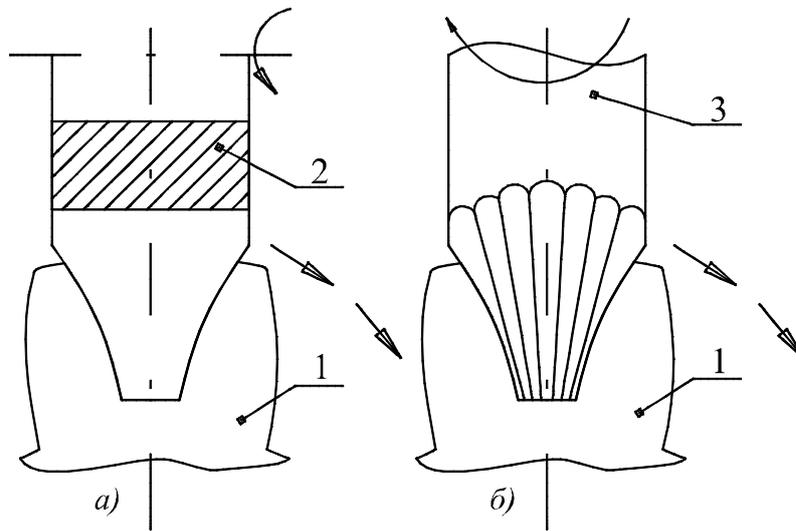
Схемы фрезерования цилиндрических колес методом копирования:
